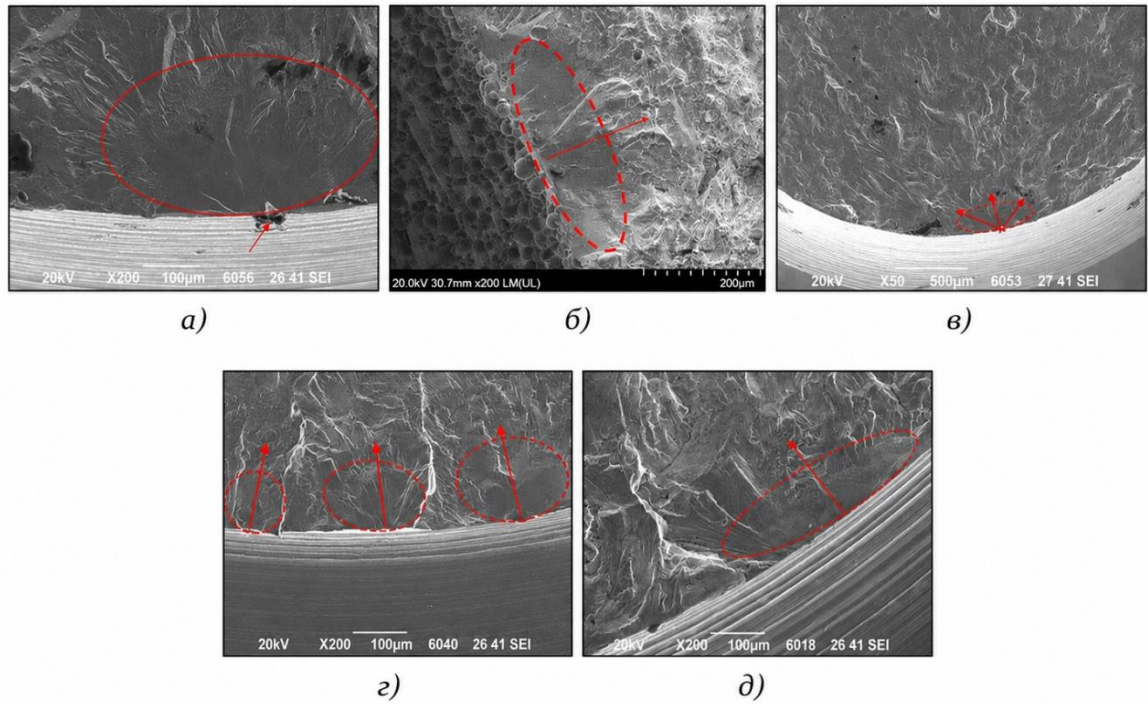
Очаг разрушения образцов: а – без концентратора напряжений; б – тонкостенный образец с технологической шероховатостью; в – с надрезом С-типа; г – с надрезом V-типа; д – с надрезом U-типа
